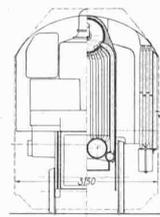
Ausführungsform der Wiesinger Lokomotive mit quer eingebautem Fahrmotor.
